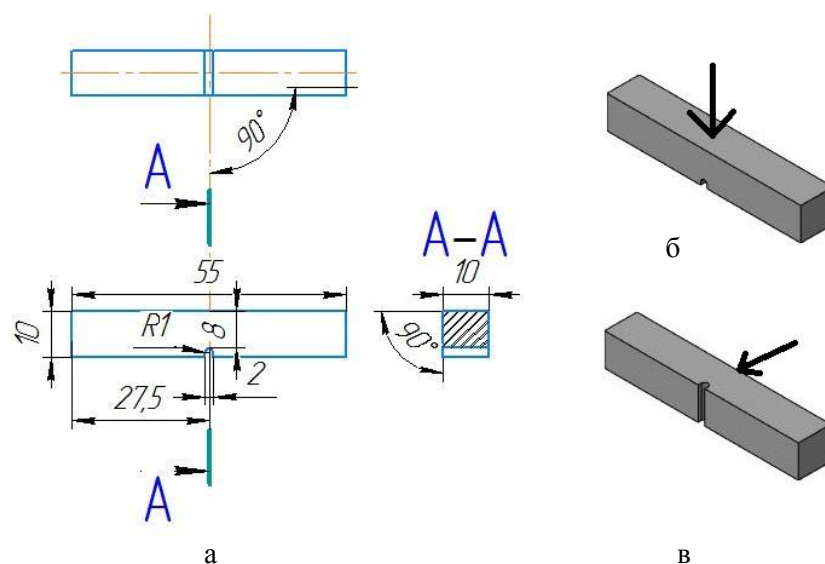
Чертеж образца и схема механического испытания на ударный изгиб:
